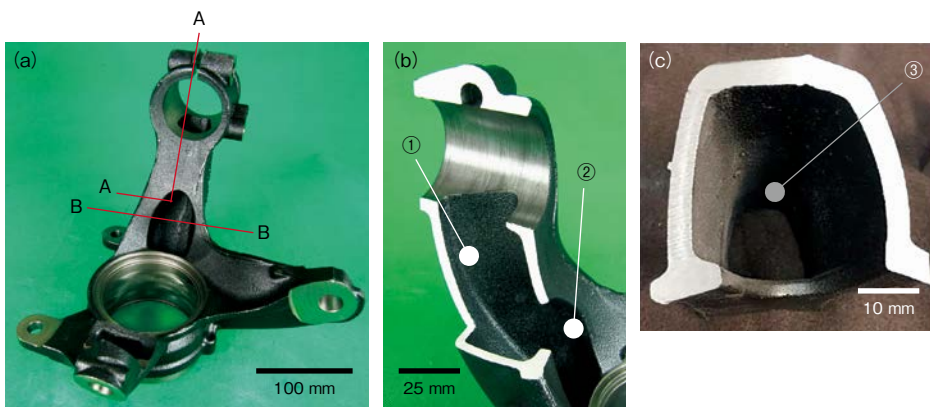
デザインの特徴 (a) 外観 (b) A-A 断面図 (c) B-B 断面図
